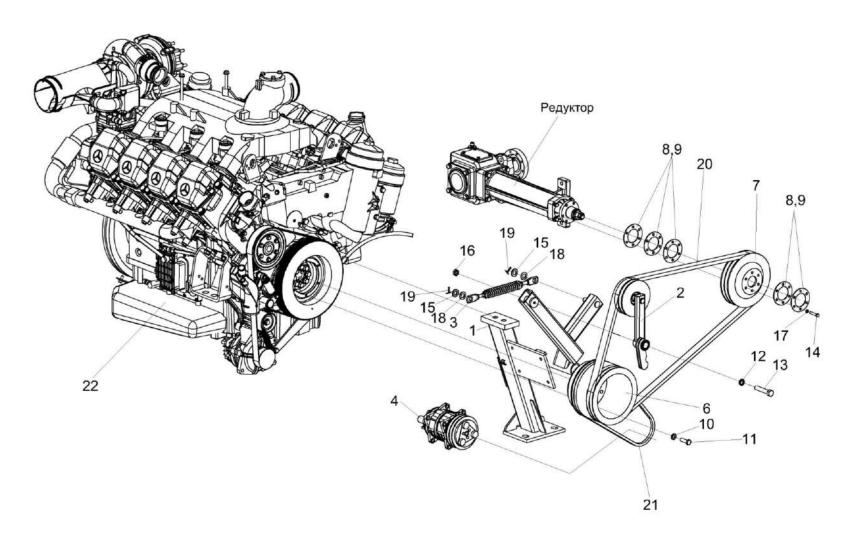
Установка двигателя ОМ 502LA КВК 0150000 (установка ременных приводов)
